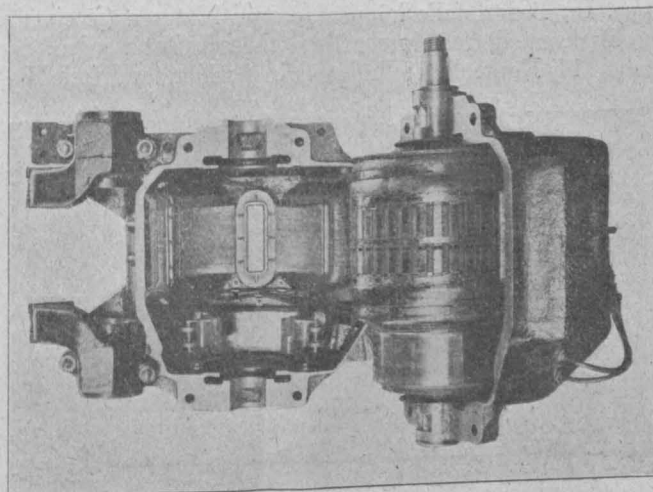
Bahnmotor, Gehäuse aufgeklappt
